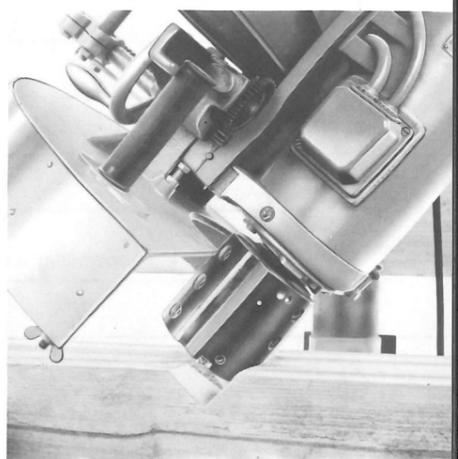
Fräsen mit geneigter Motorwelle. In gleicher Stellung können auch mit einem Sägeblatt Fasenschnitte ausgeführt werden.
